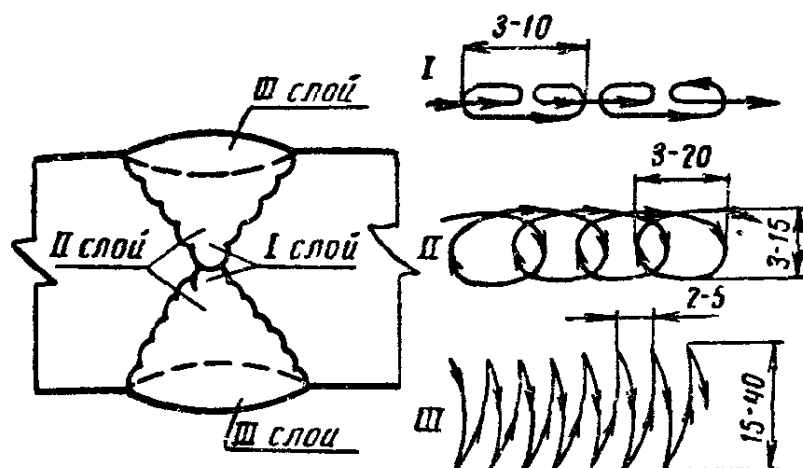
Перемещение конца проволоки при полуавтоматической сварке X-образного шва в среде углекислого газа
